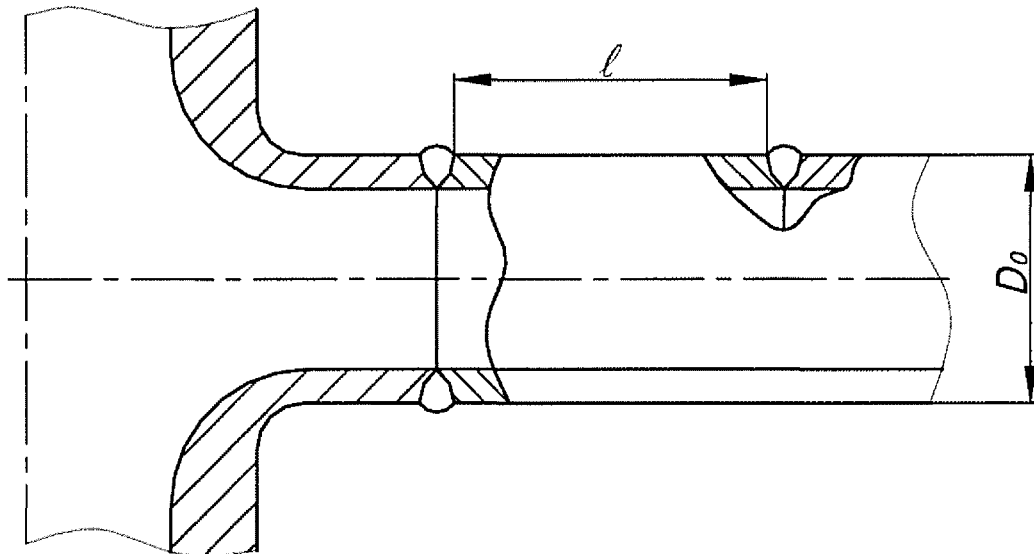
Расположение сварных соединений приварки деталей к оборудованию и трубопроводам
